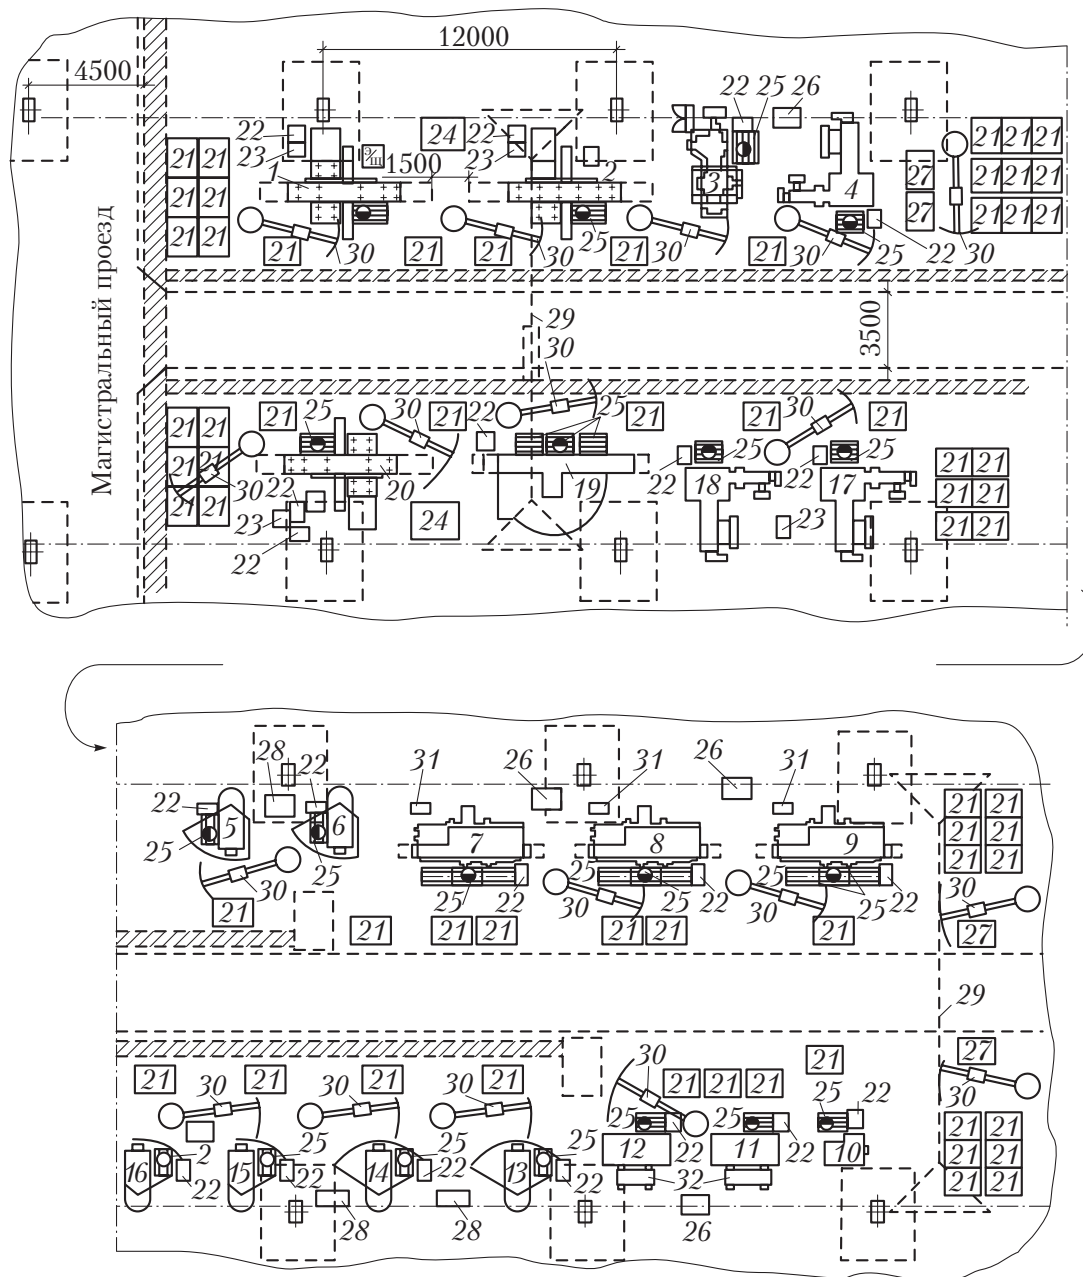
Пример планировки переменнo-поточной линии по обработке корпусных деталей:
